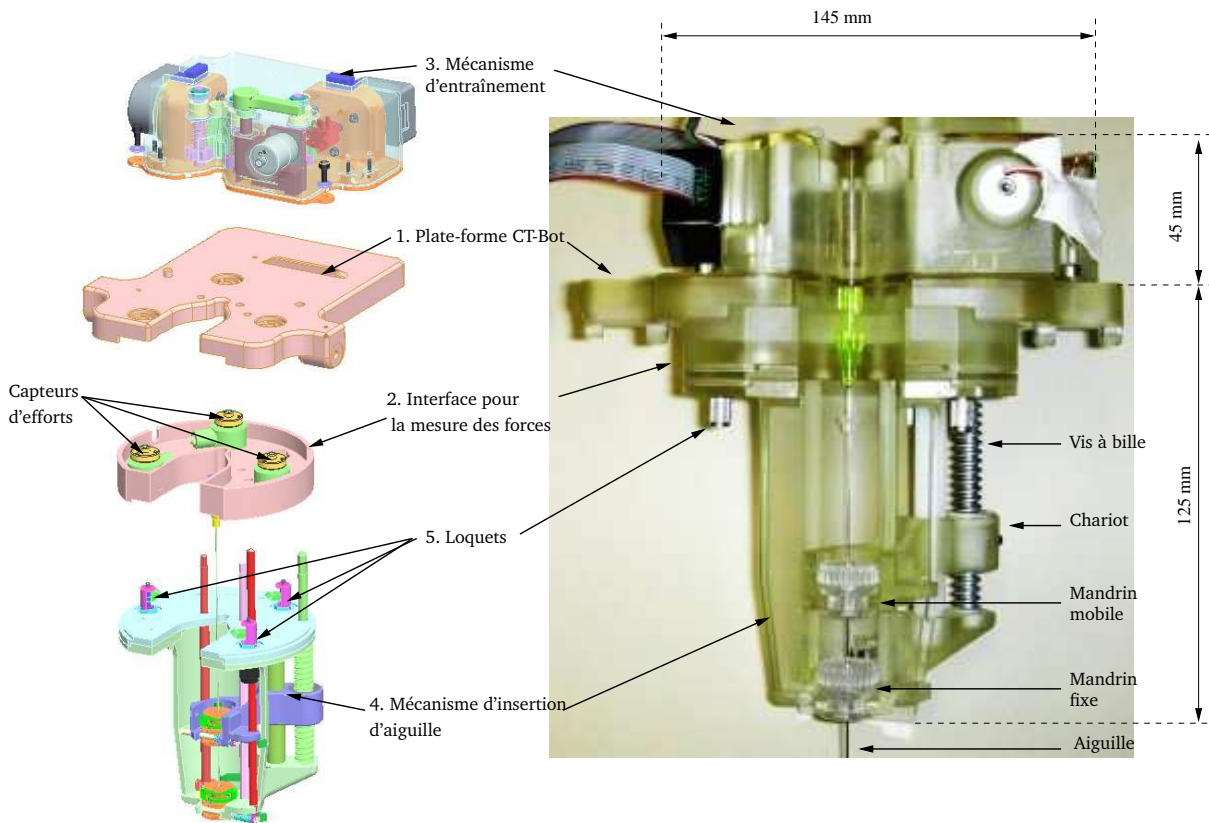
Vue CAO éclatée et prototype de la première version du système porte-aiguille.
